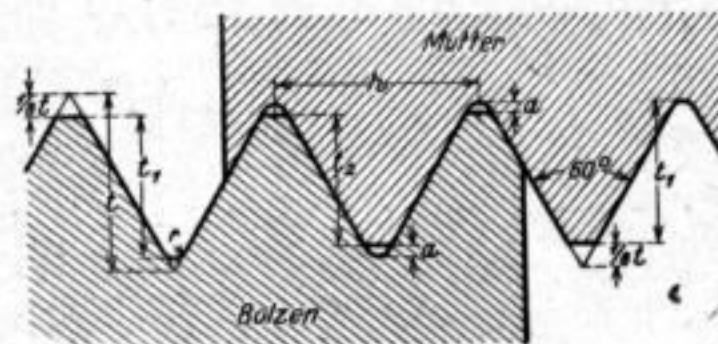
Profil des Schweizer Uhrmachergewindes für Schrauben von 1 mm Durchmesser an (Profil des Schweizer metrischen Gewindes)
